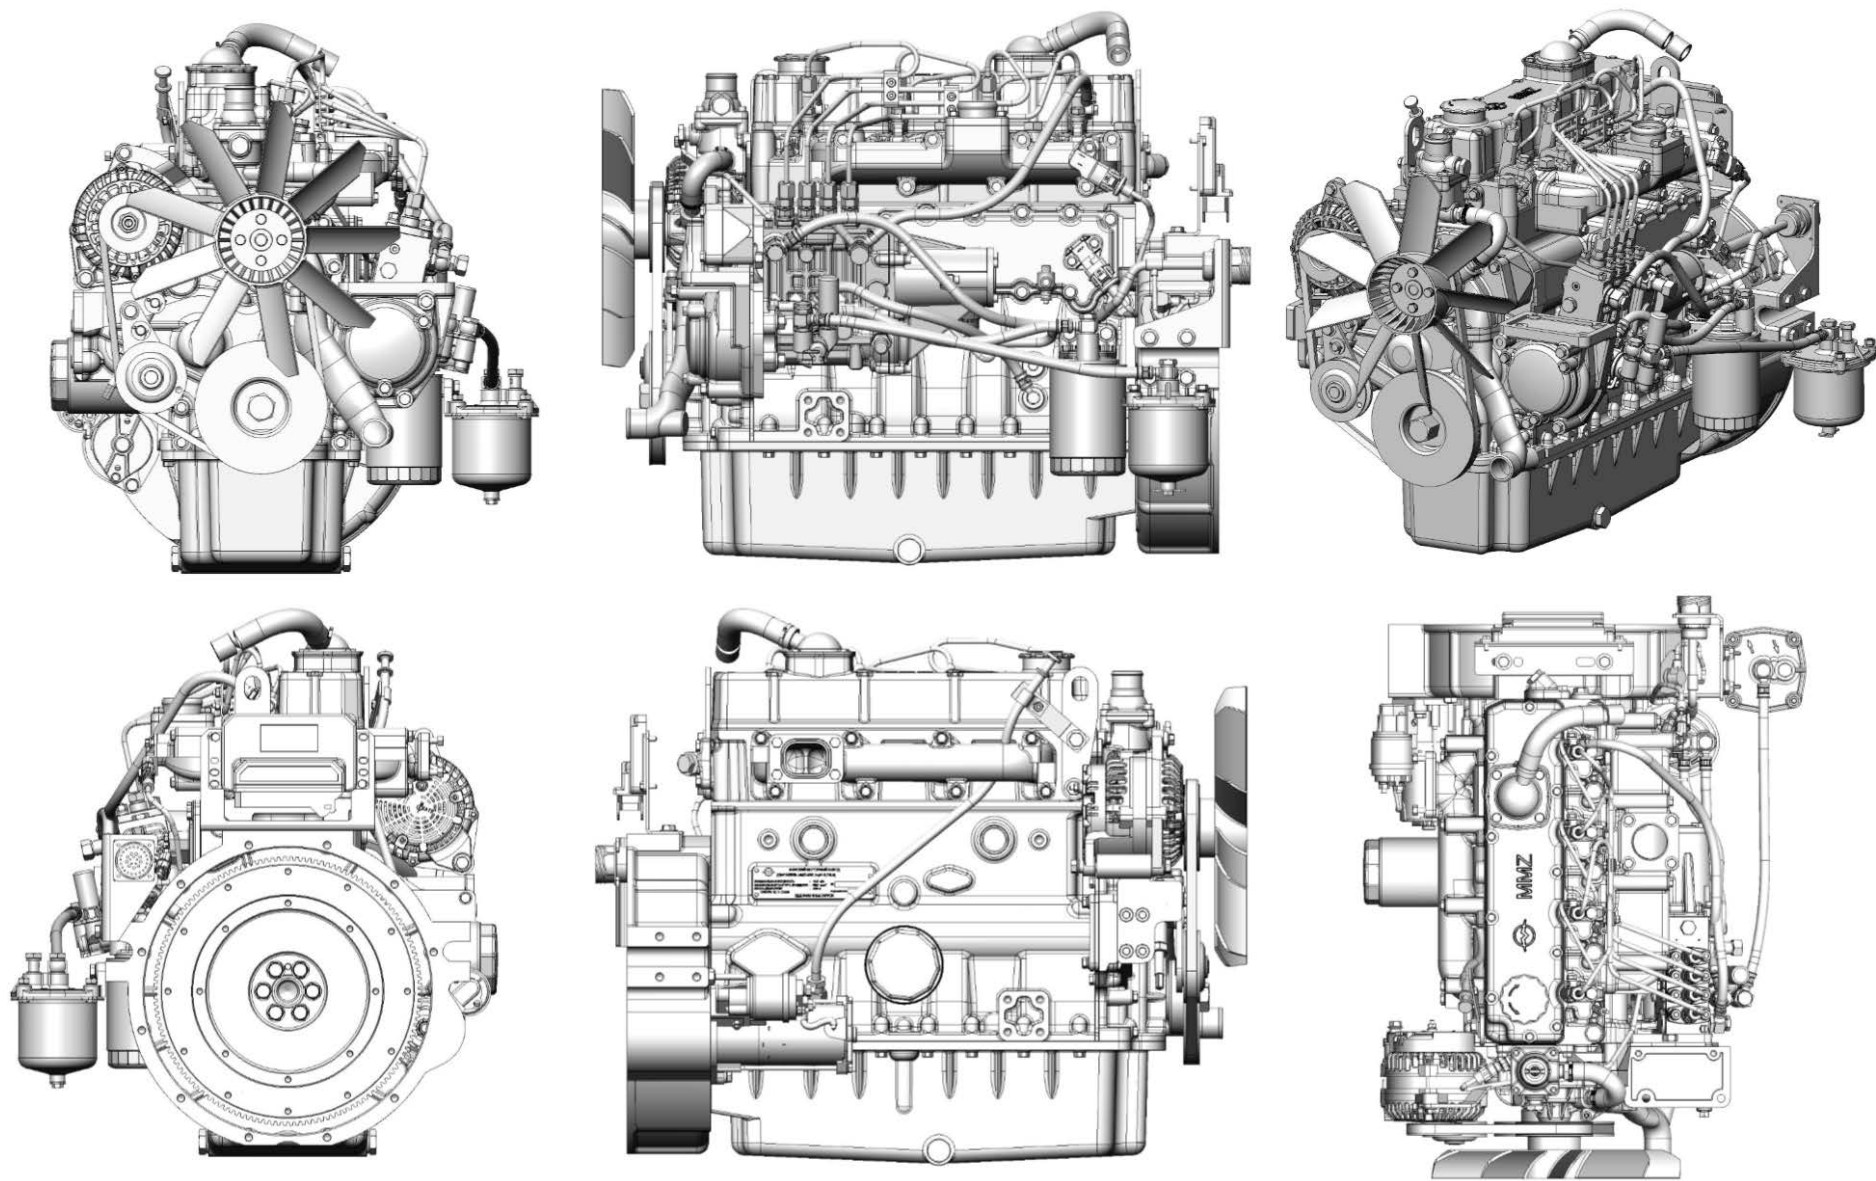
Общий вид двигателя MMZ-4DG.1-00
